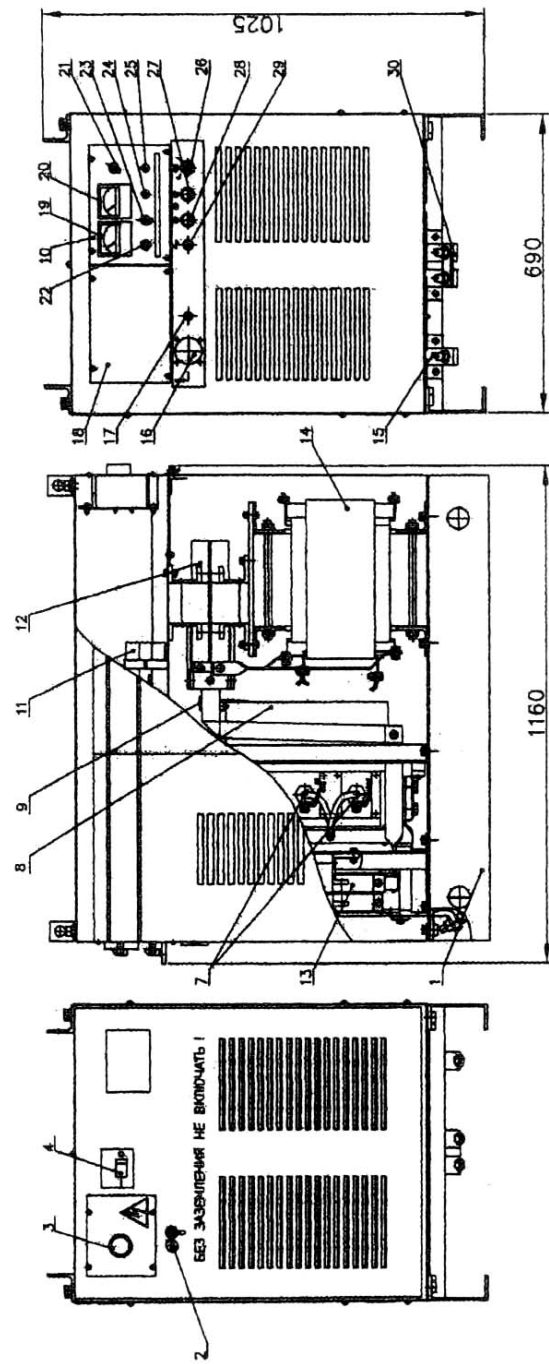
Общий вид сварочного выпрямителя ВДУ
